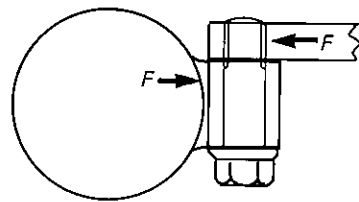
Die Befestigung des Bremssattels mit einem Bolzen in einem einzigen Arm.
